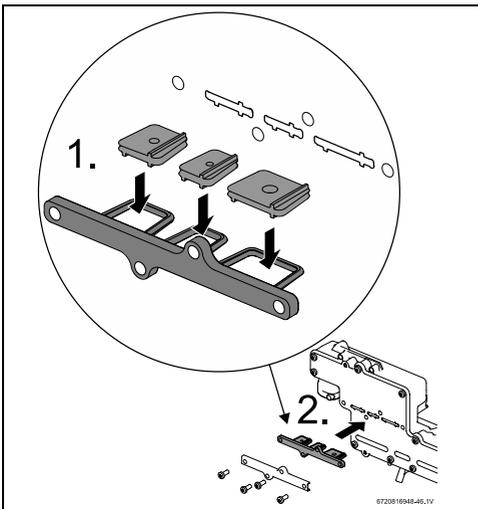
Assemblage de conversion de gaz pour l'appareil 160kBTU
